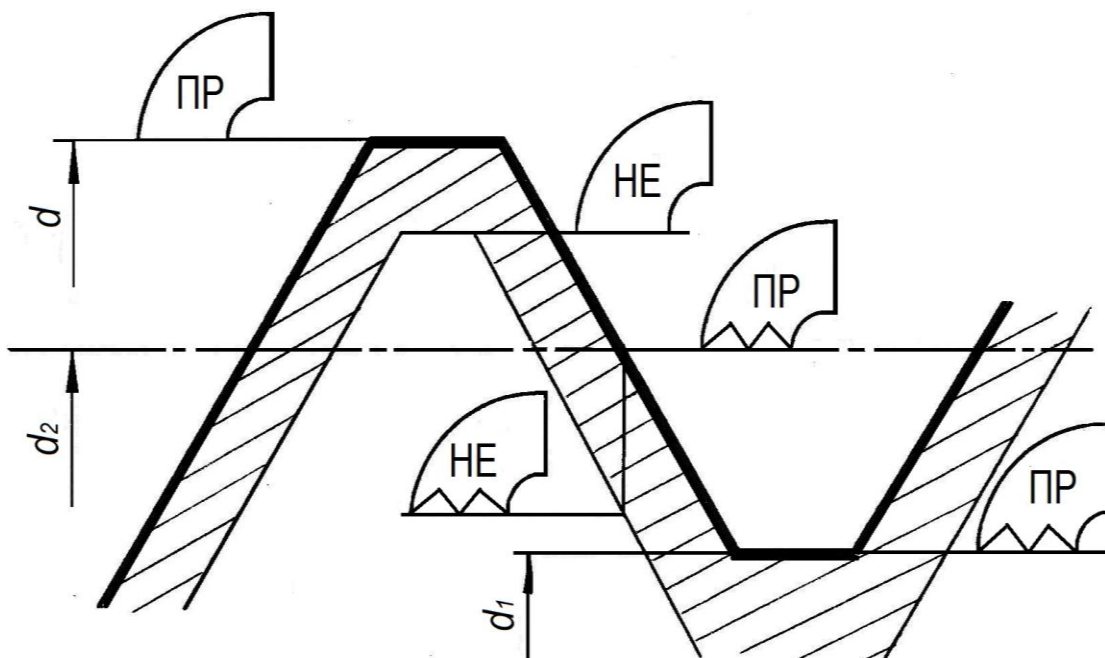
Схема контроля предельными калибрами внутренней резьбы
